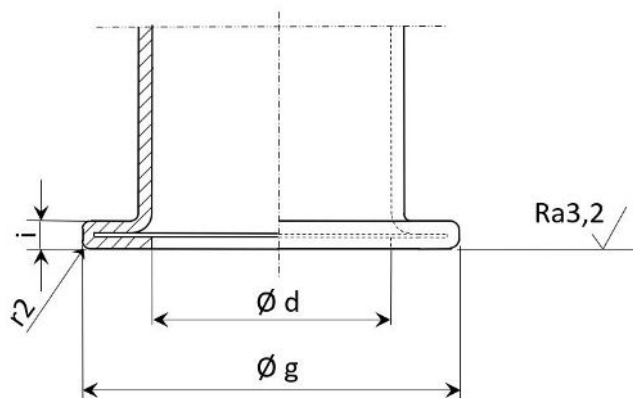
Rabattement de collerette d'adaptation à l'installation existante
